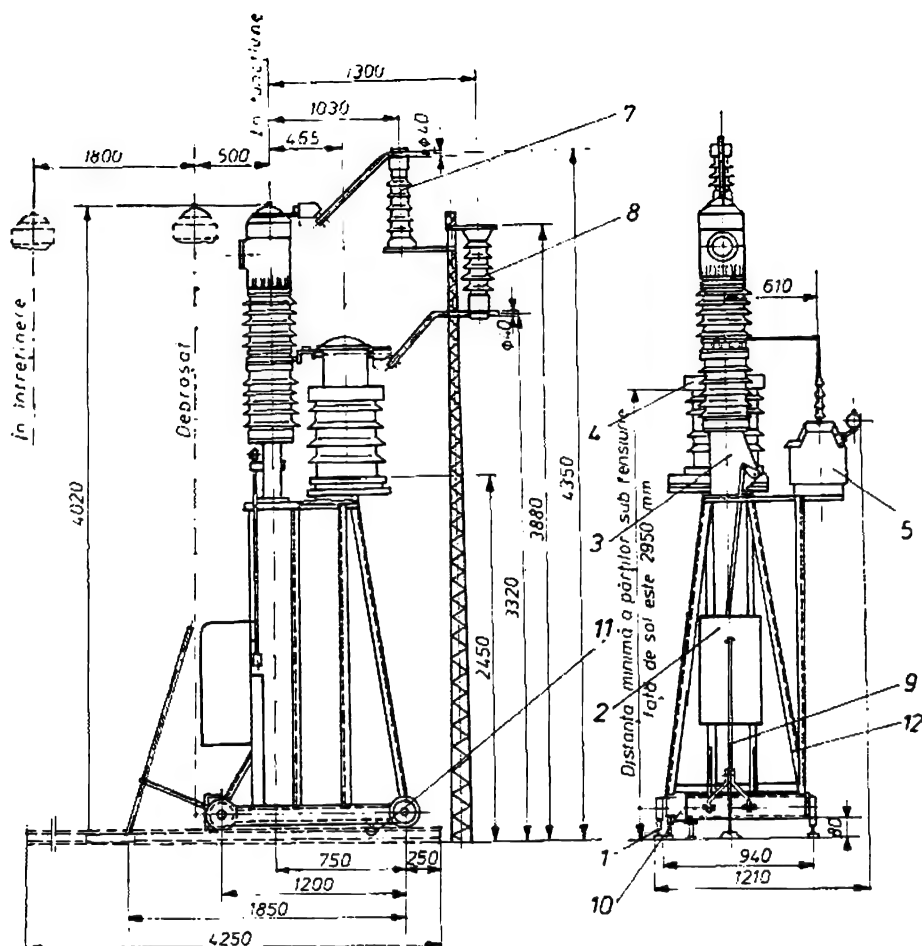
Înteruptoare IUP-25/1250 cu CESU 35/600, 1000 și TEBU 25/0,1. Dimensiuni de gabarit:
